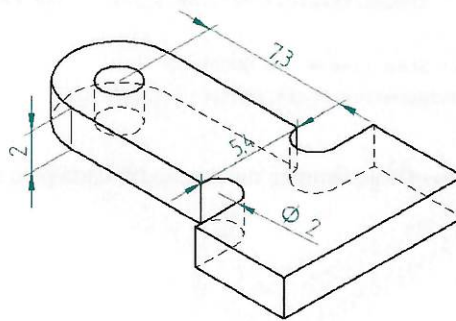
Dimensões em (mm) da viga para simulação
